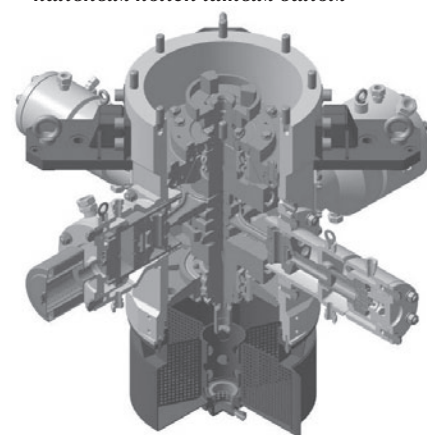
Разрез четырехрядного компрессора с вертикальным коленчатым валом
